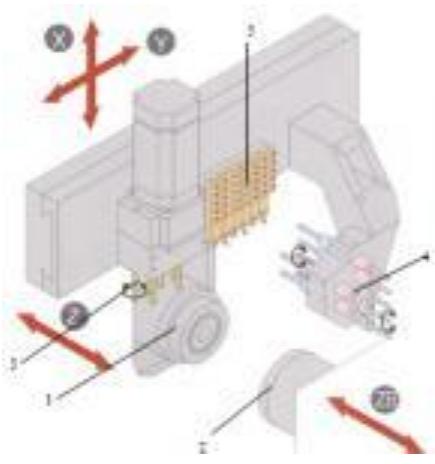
Компоновка станка Diamond 20CS:
